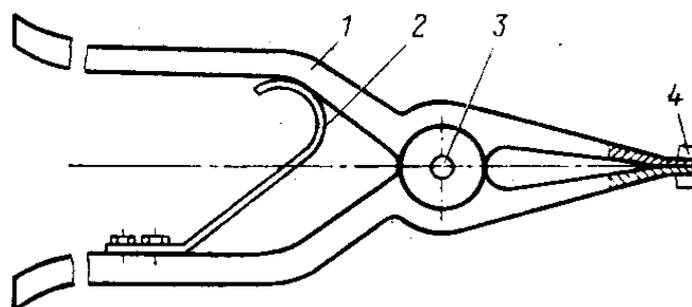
Съемник для поршневых колец: 1 – рычаг; 2 – пружина; 3 – ось; 4 – губка
